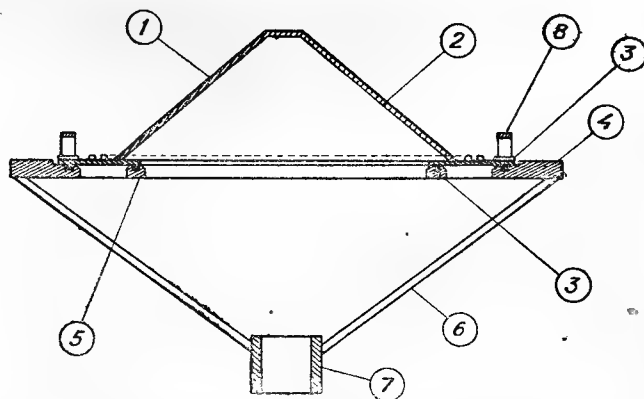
Головка аппарата для отливки диффузоров без шва: 1 — частая сетка с'емки части матрицы; 2 — дыропробивная сетка с'емки части матрицы; 3 — уплотняющее резиновое кольцо; 4 — поддерживающее кольцо; 5 — ребра поддерживающего кольца; 6 — нижний конус; 7 — втулка для присоединения головки к вакуумному насосу; 8 — ручка
